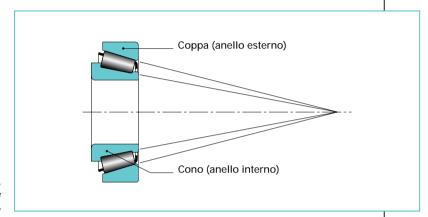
Il disegno "on-apex" produce un moto di puro rotolamento in tutti i punti lungo il corpo del rullo
